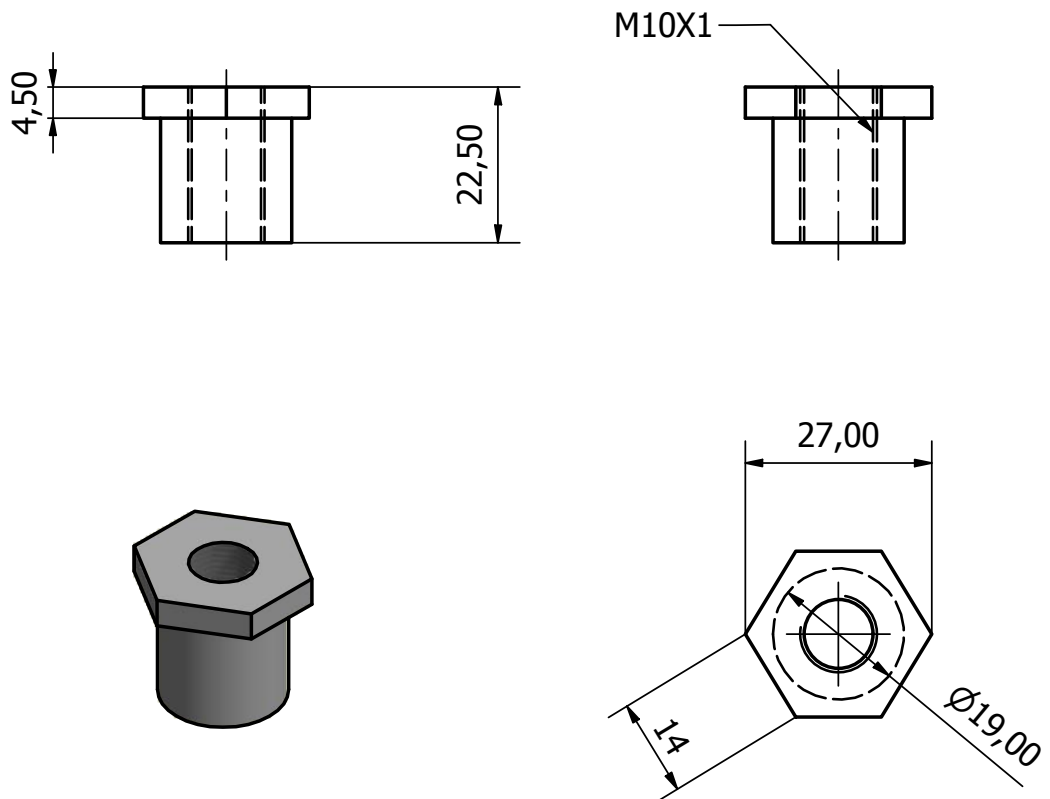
Diseño para la pieza de tubería para la medición de la presión.
